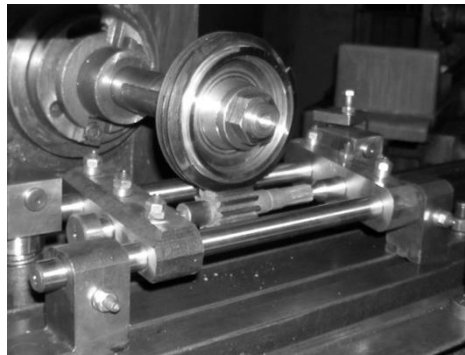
Установка оброблюваної деталі і інструмента на верстаті
